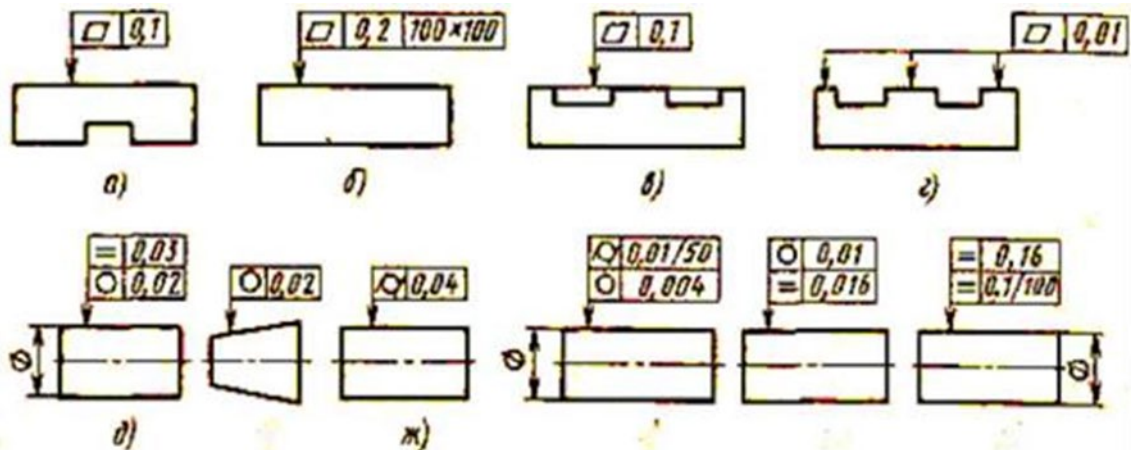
Условные обозначения допуска формы поверхностей детали
